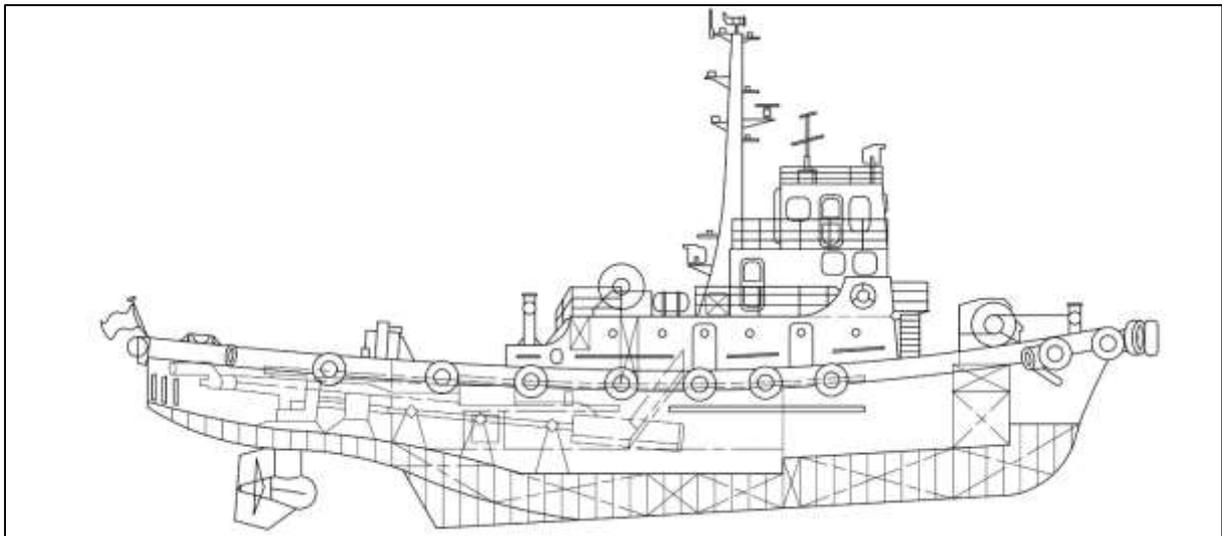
Perfil longitudinal del buque Rua II. Fuente: plano de arreglo general
